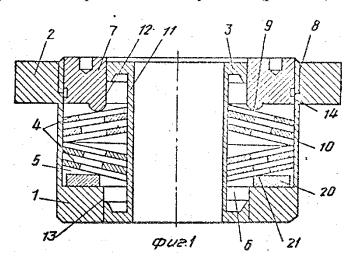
Кондукторная втулка (патент SU1328085)
